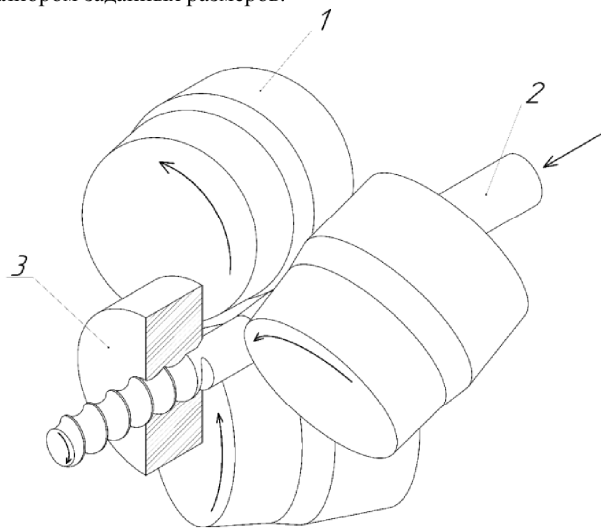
Совмещенный способ получения арматурного профиля: 1 – прокатные валки, 2 – заготовка, 3 – матрица
